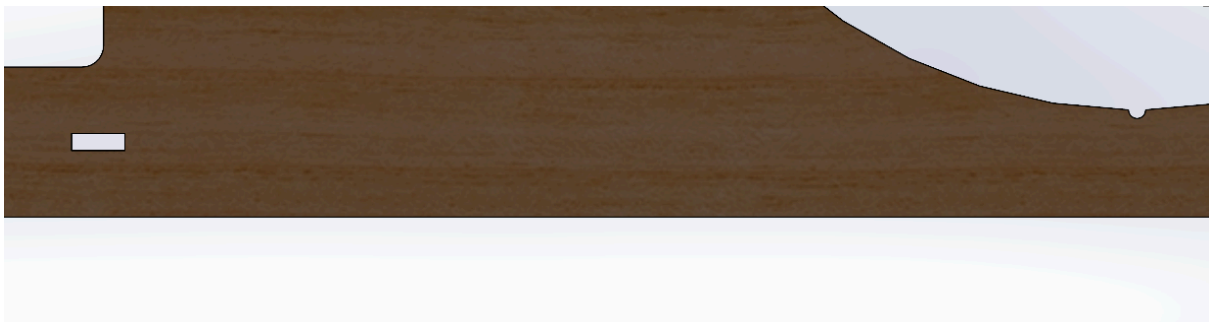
Detalle del Tablero Inferior (Fuente: Elaboración Propia)
